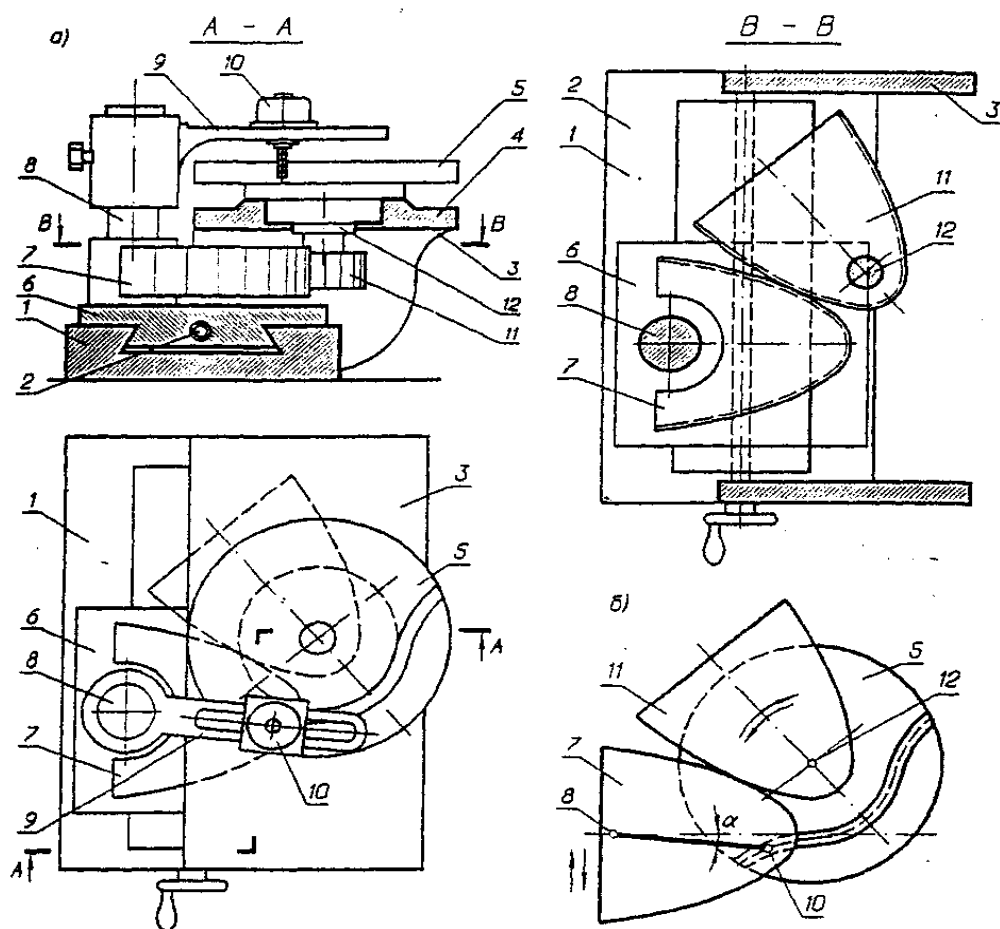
Конструкція верстатів для фрезерування криволінійних пазів
